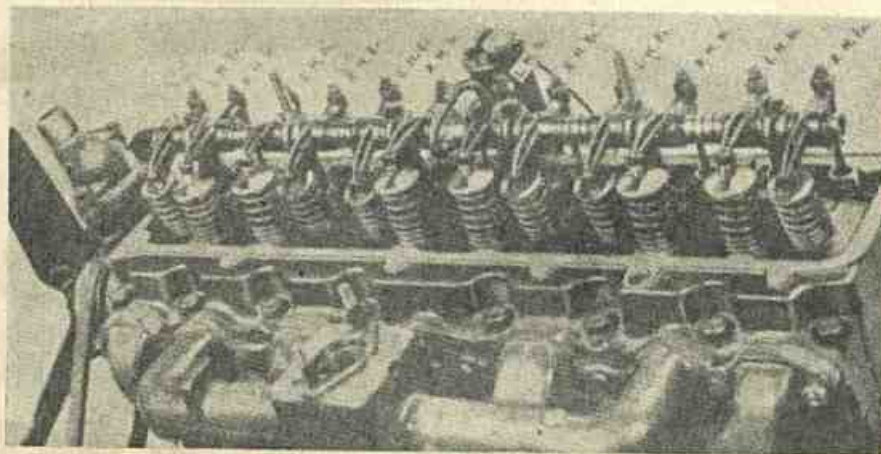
Conjunto de braço oscilante num motor de 6 cilindros de válvulas elevadas.
